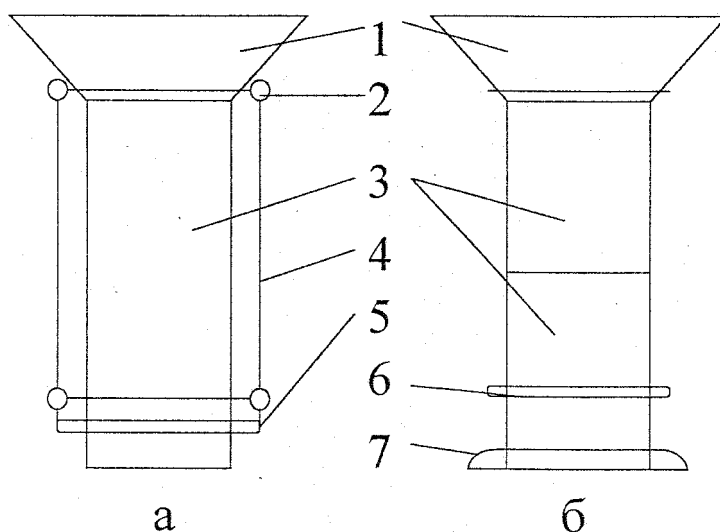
Конструкции гильз-воронок для формирования полиэтиленового рукава в "гармошку":
